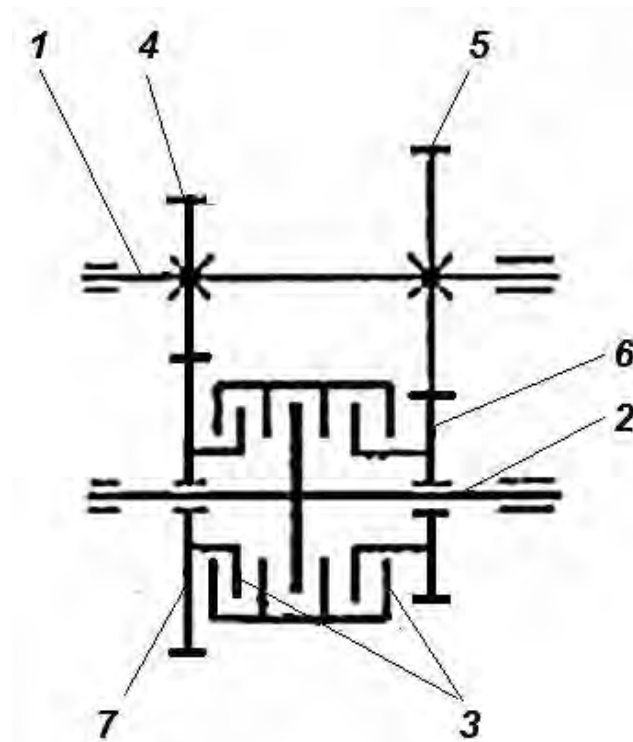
Принципова схема коробки передач з керуванням гідроідтискними муфтами [40]:
